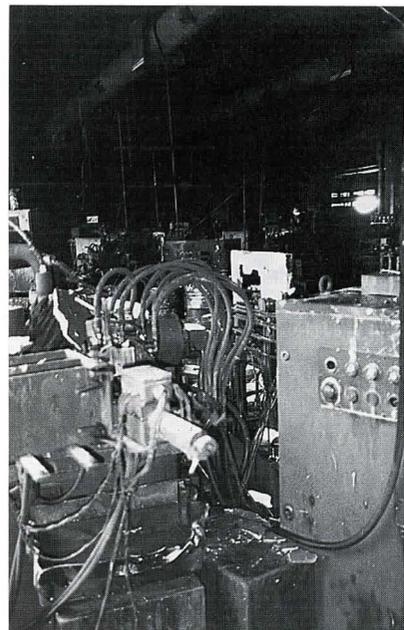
Blick in die Halle. Mehrere Werkzeugmaschinen wurden durch den Brand beschädigt.
